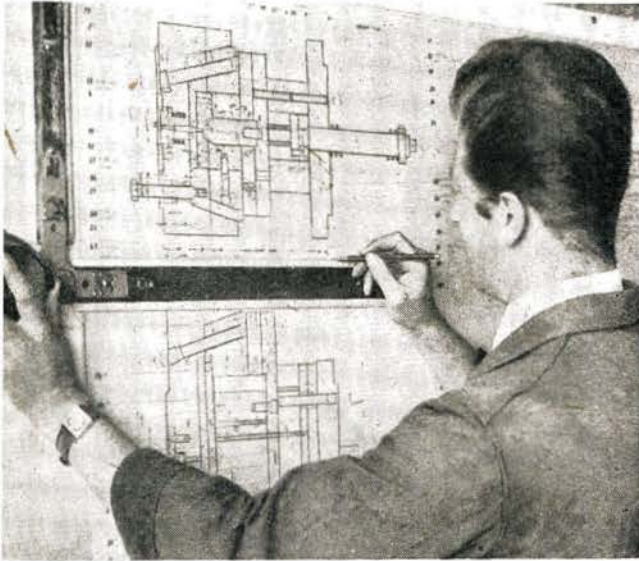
Auf dem Reißbrett entstehen die Werkzeugkonstruktionen.
